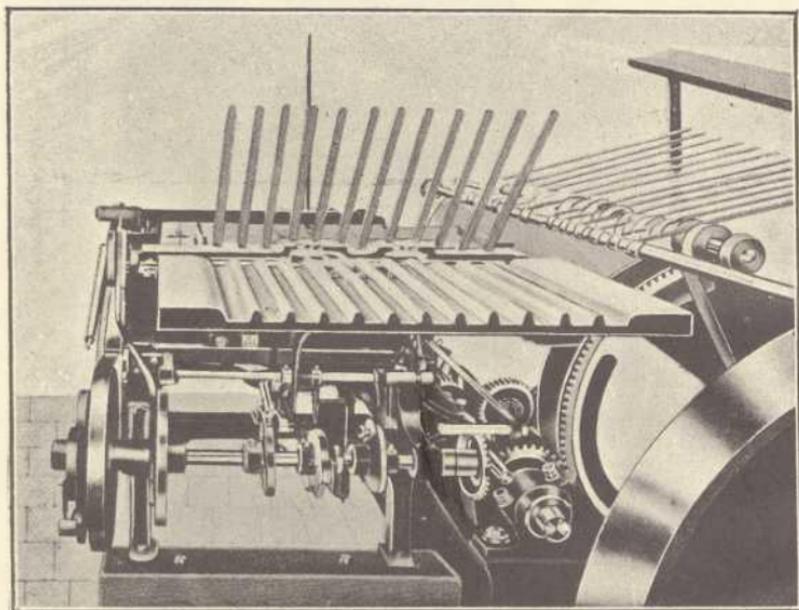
Plegadora automática, acoplada a una máquina de imprimir cilíndrica.
